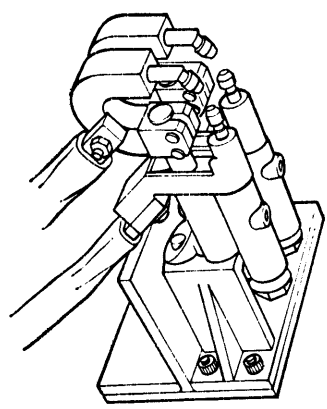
Сдвоенные сварочные клещи для роботизированной точечной сварки
